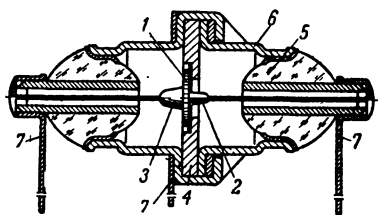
Устройство плоскостных триодов типов П1 и П2. 1 — германий; 2 — эмиттер (индий); 3 — коллектор (индий); 4 — держатель; 5 — стеклянный изолятор; 6 — корпус; 7 — вывод.
